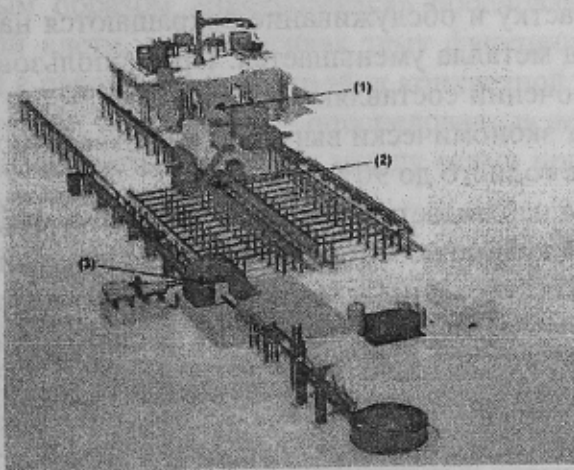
а – Общий вид технологического процесса Cast and Roll (1 - непрерывное литье полой заготовки, 2 – обработка поверхности заготовки, 3 – планетарная винтовая прокатка)
